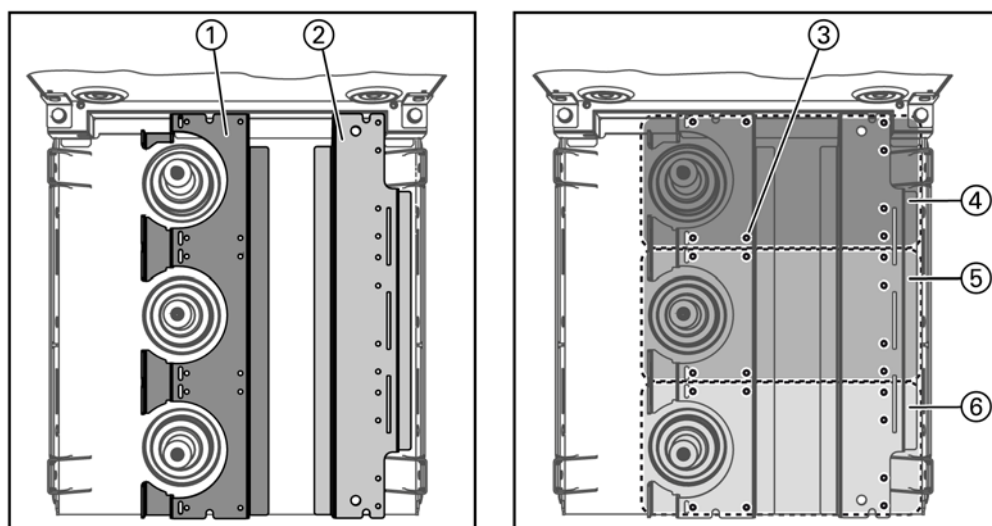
Крепление трансформатора напряжения (вид сверху)
